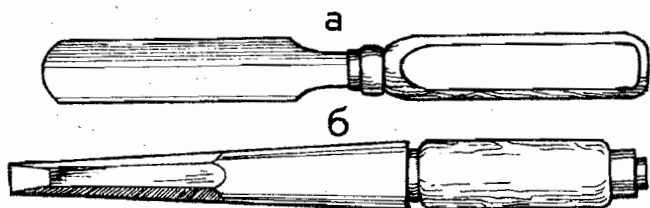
Инструменты для долбления отверстий: а — стамеска; б — долото.
